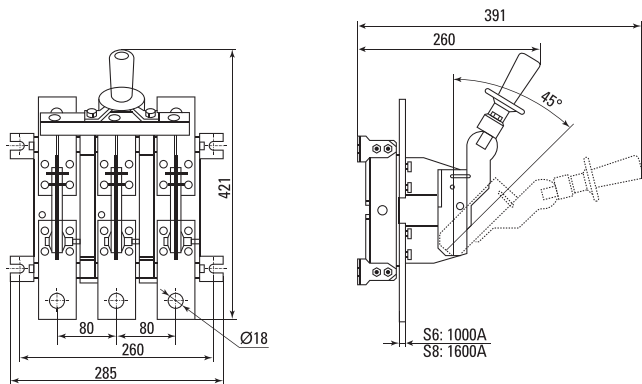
Габаритные и установочные размеры разъединителя типа PE19-41/43 с центральной рукояткой
